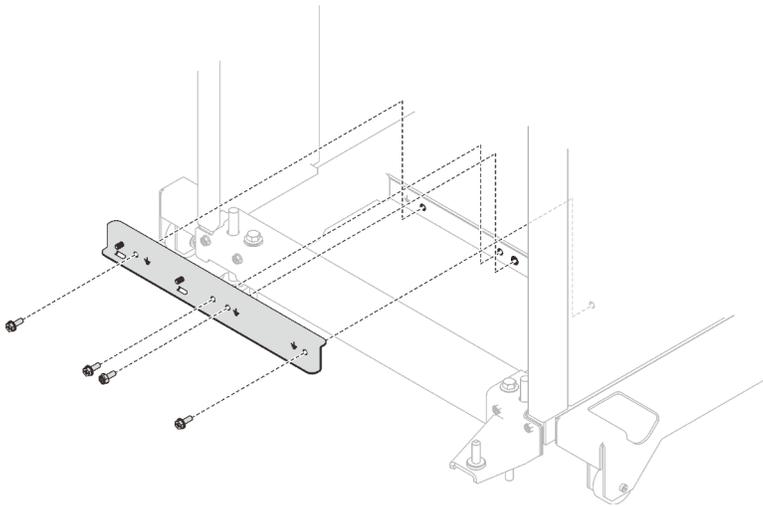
Entfernen der unteren Montagehalterung für die Rackleitung
